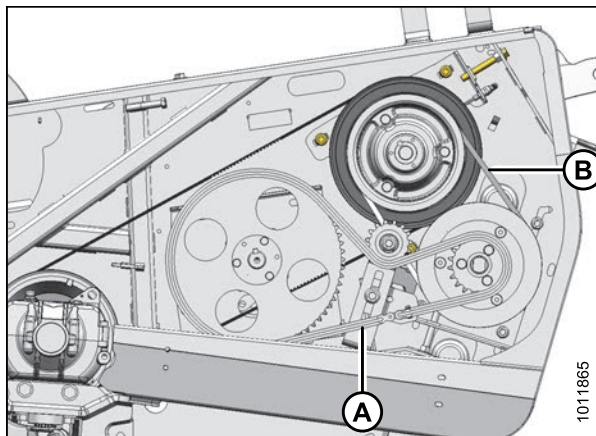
Ремень привода ножа и цепь привода жатки
